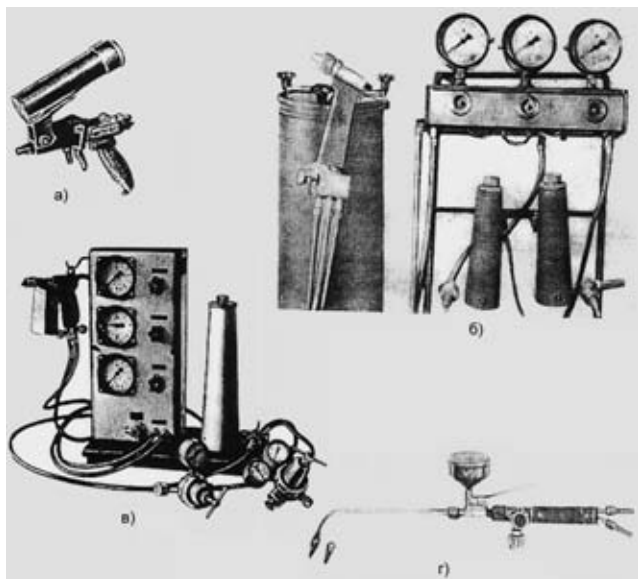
Горелка для порошкового газопламенного напыления (а); газопламенная установка УГТП для ручного и механического нанесения газопламенных покрытий из тугоплавких порошковых материалов в любом пространственном положении (б); газопламенная установка УГТП для ручного нанесения покрытий из порошковых материалов с температурой плавления 800—1500 °С (в); горелка типа ГН (ГН-1, ГН-2, ГН-3) для наплавки гранулированных самофлюсующихся твердых сплавов на основе хром—бор—никель—кремний или других композиций с размером частиц 0,04—0,10 мм с целью упрочнения или восстановления рабочих поверхностей деталей машин (г)
